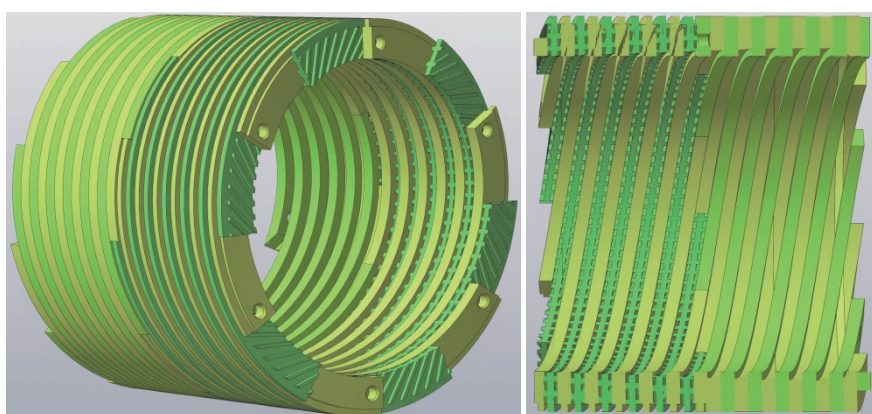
Общий вид сборки сепаратора из контр-винтовых шайб
